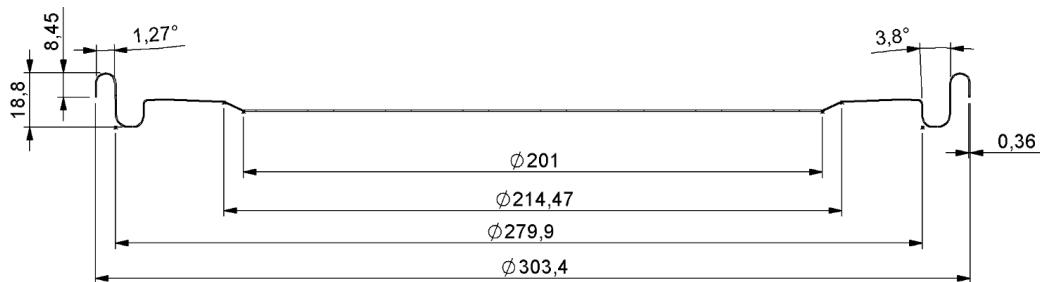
Dimensões da tampa metálica (Autor, 2024).
